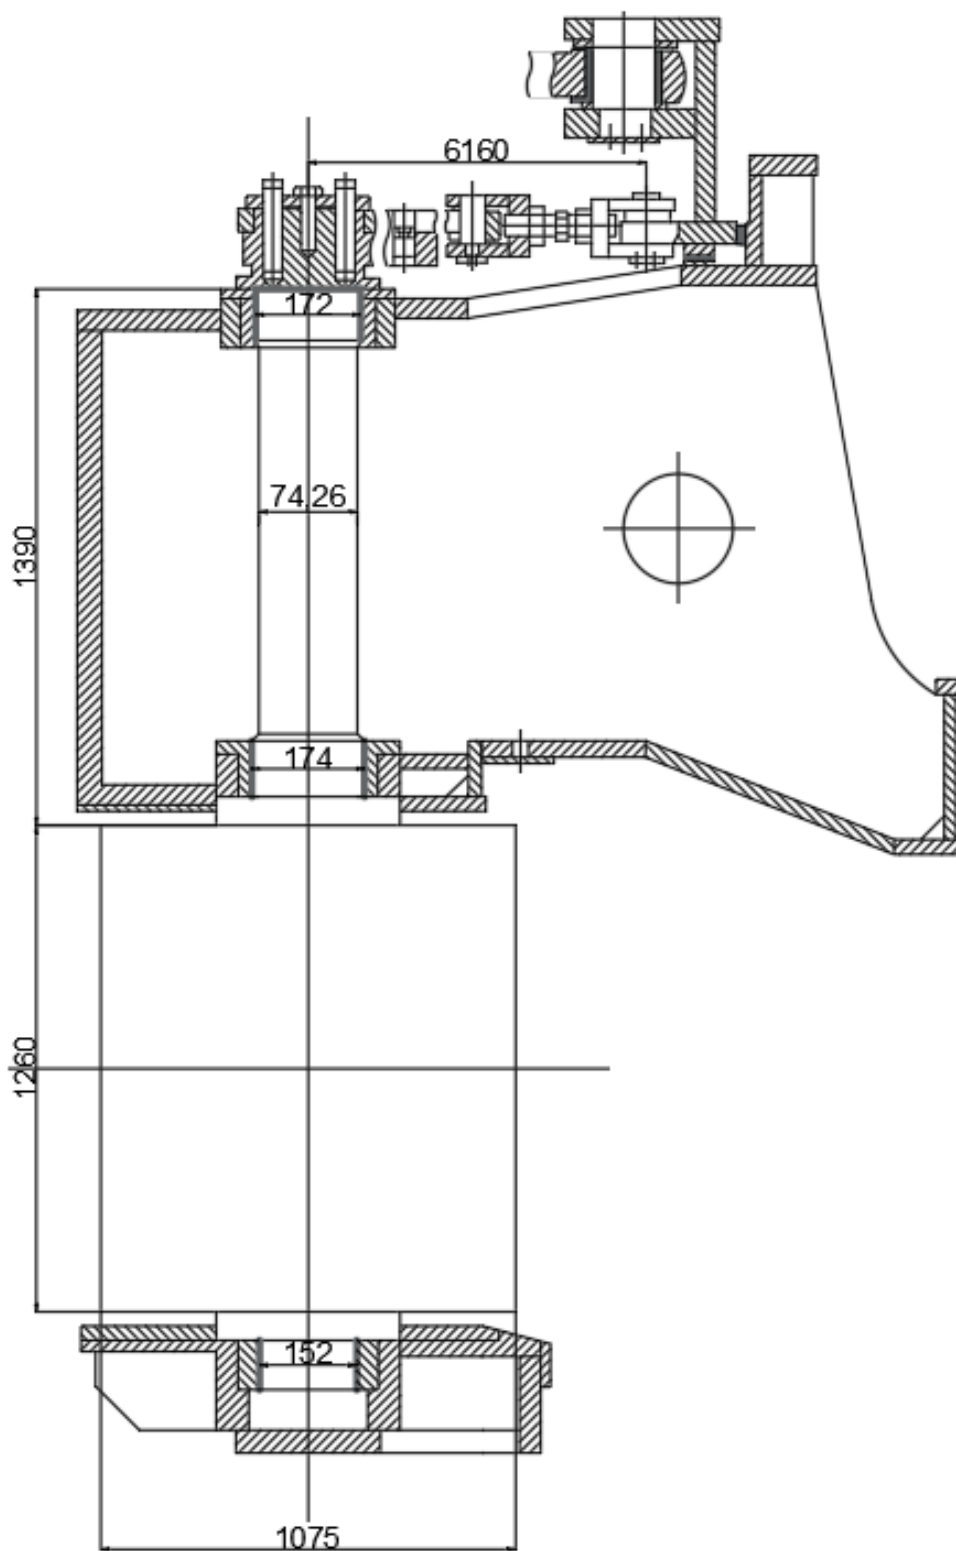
Разрез лопатки направляющего аппарата и механизма поворота
